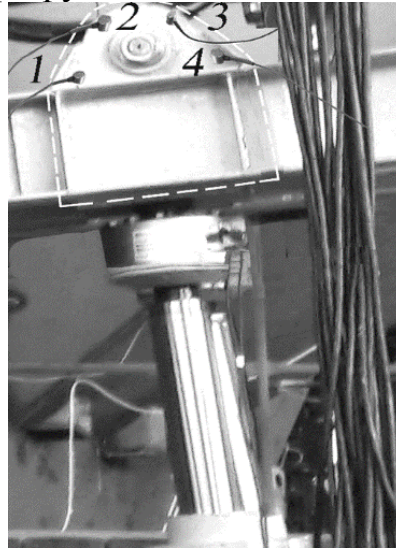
Вид слева кронштейна опорного вала подъемного механизма; - - - – область АЭ контроля левого кронштейна опорного вала подъемного механизма; 1, ..., 4 – места установки ПАЭ
